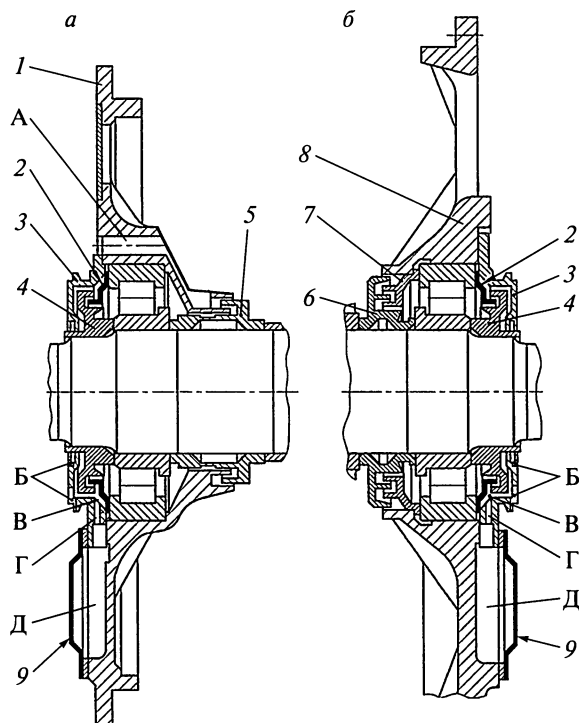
Подшипниковый узел № 1 тягового двигателя НБ-514Е:
